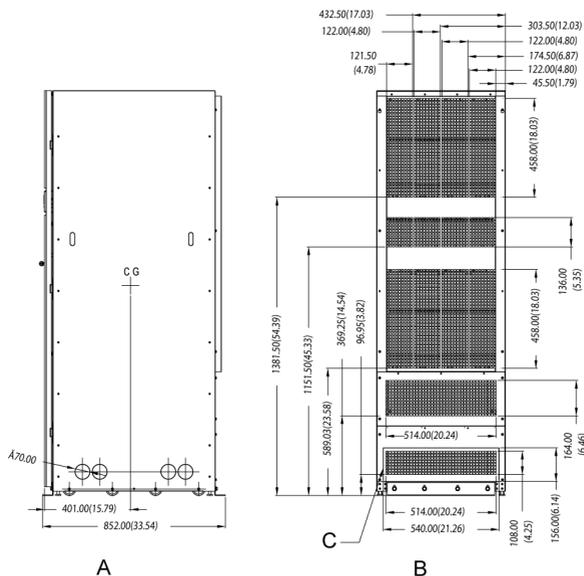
Габаритные размеры шкафа ИБП 93Е на 160-200 кВА (вид сзади и справа)
